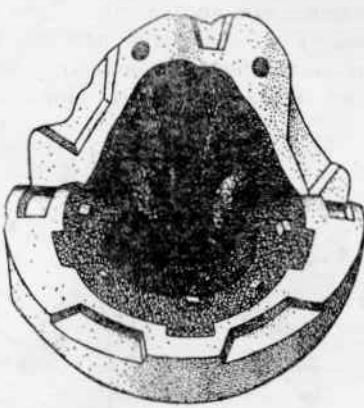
Клеевая форма и отливка черепа. Лицевая и верхняя части формы, сложенные вместе.
